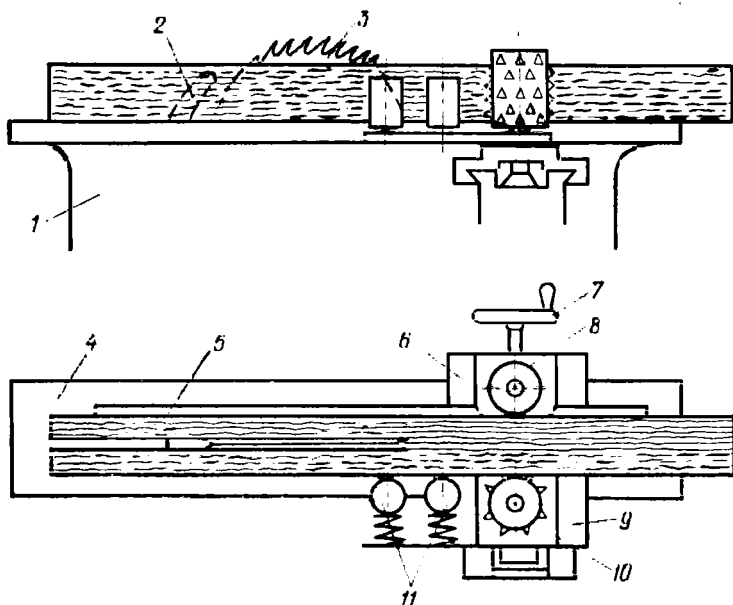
Схема круглопильного ребрового станка ЦР-4А:
